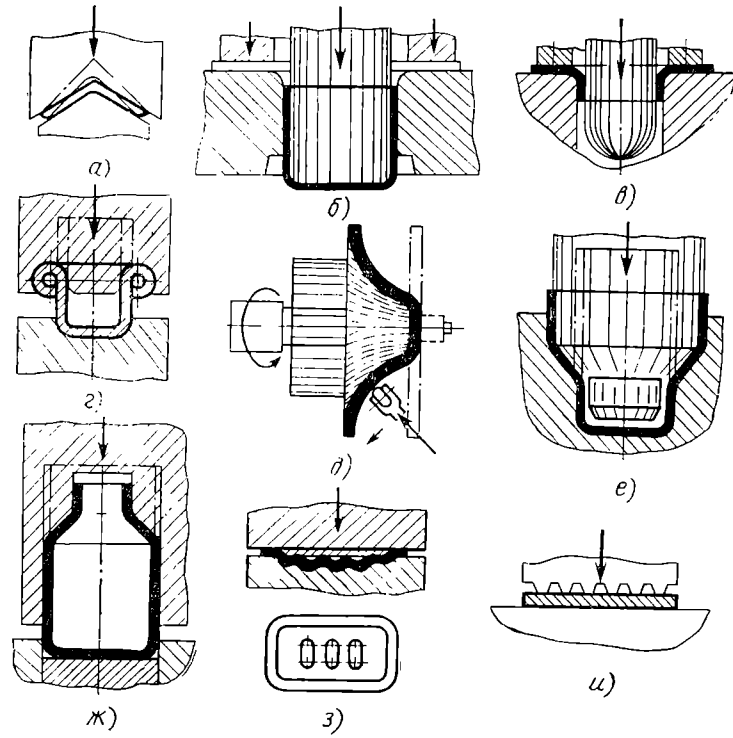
Формоизменяющие операции листовой штамповки: а — гибка, б — вытяжка, в — отбортовка, г — закатка, д — ротационная вытяжка, е — раздача, ж — обжим, з — рельефная формовка, и — правка
